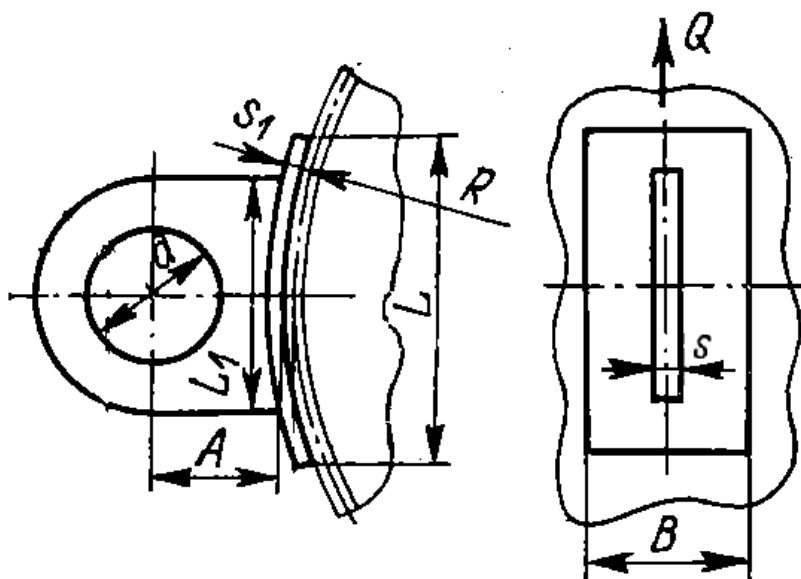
Конструкція стропувального пристрою (вушка)
